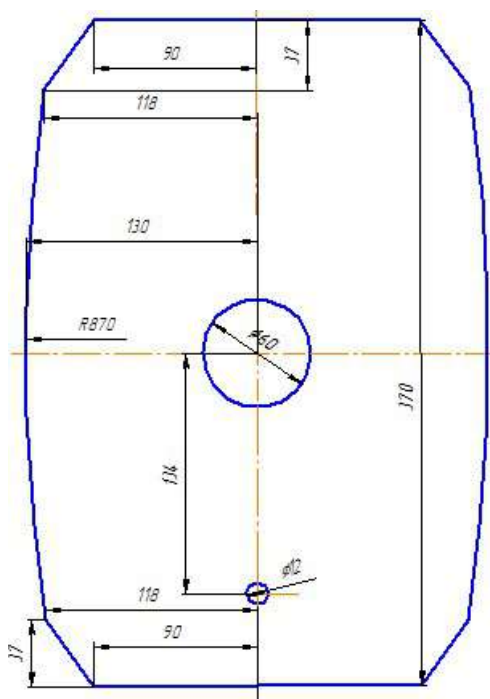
Шаблон вирубки плоскої заготовки
